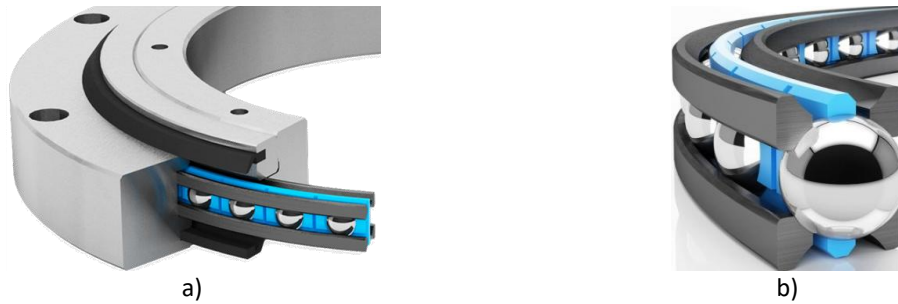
Rodamiento de alambres: a) sección del rodamiento [20] b) pista de rodadura [18].
